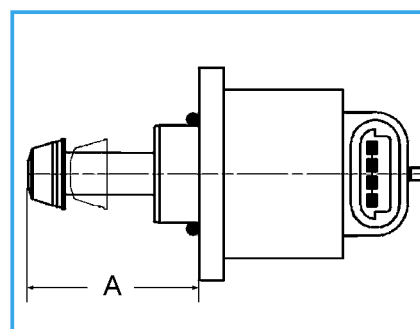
A – Mesure de réglage pour le montage provisoire de 35 à 36 mm.
